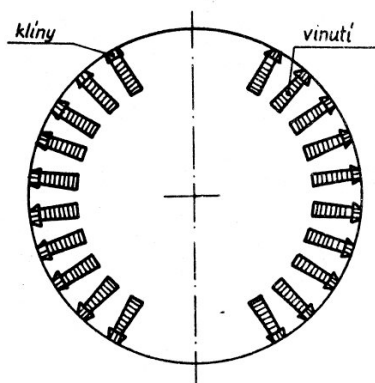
část rotoru a statoru hydroalternátoru [12]
